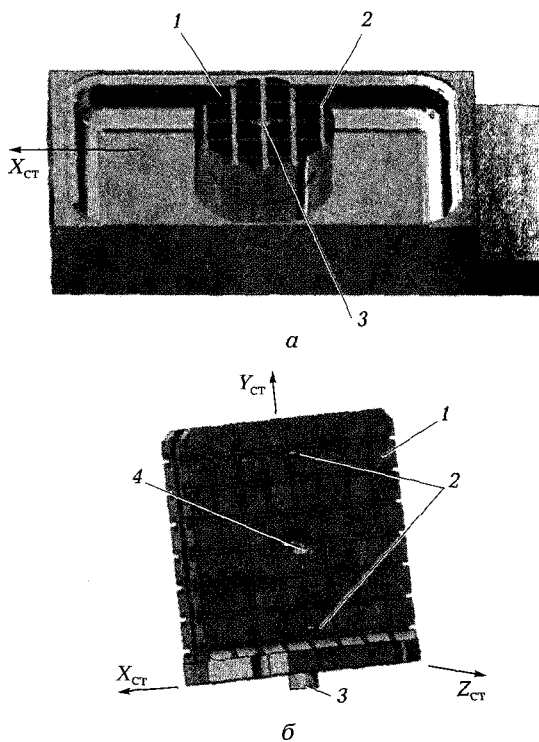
Установка приспособления на стол фрезерного станка:
